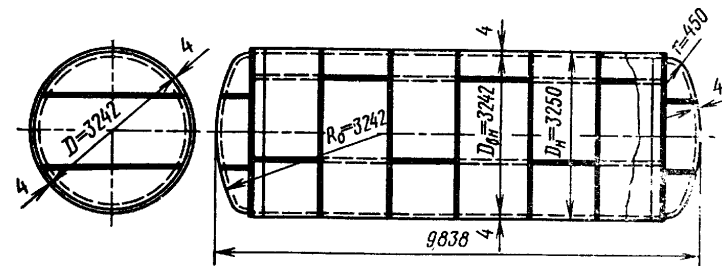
Конструкция сварной горизонтальной цистерны
